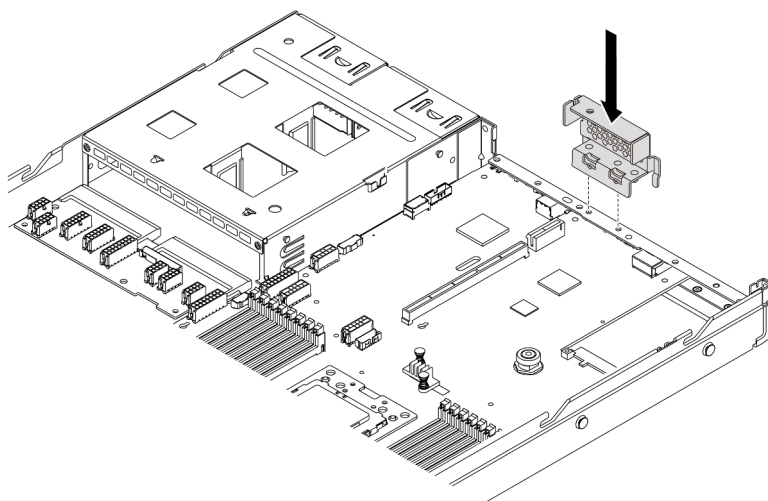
Installazione della staffa posteriore per il montaggio a parete
